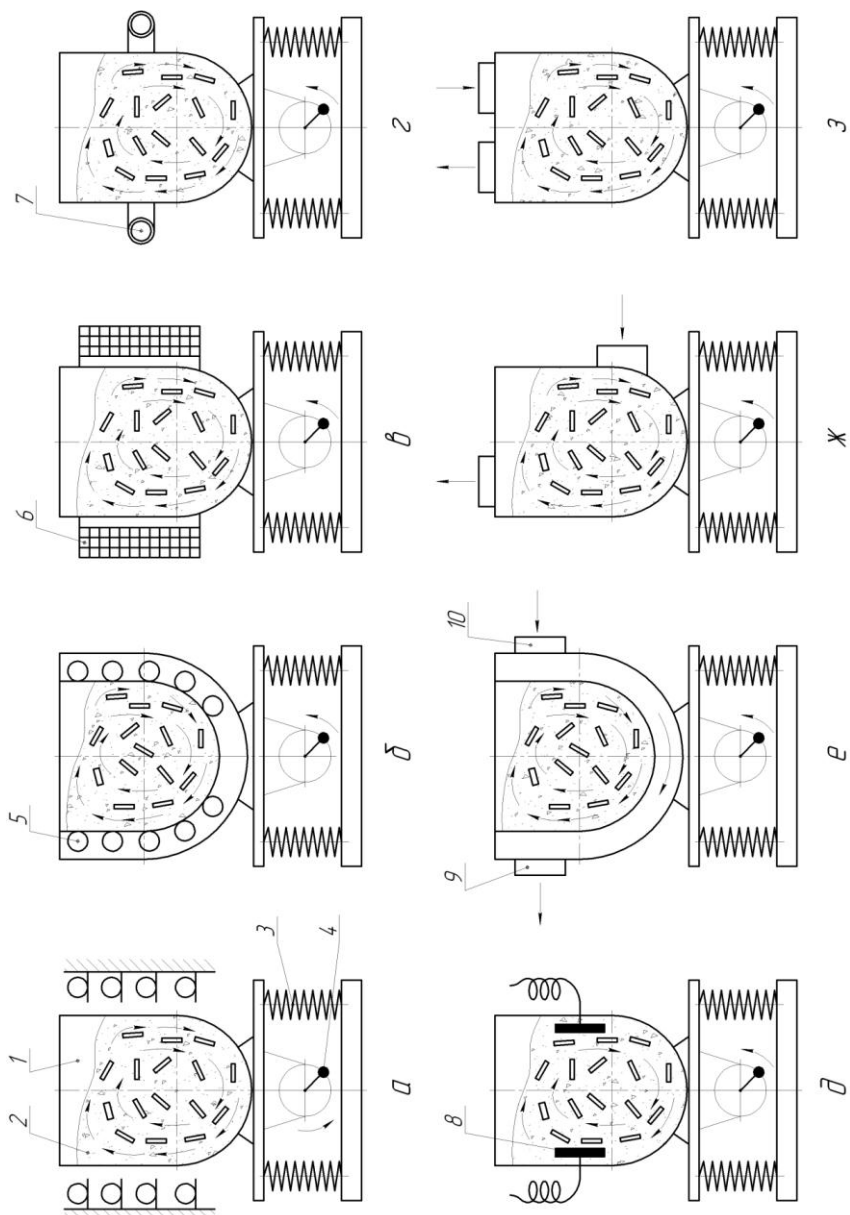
Схема резервуаров вибростанков для механотермической виброобработки
